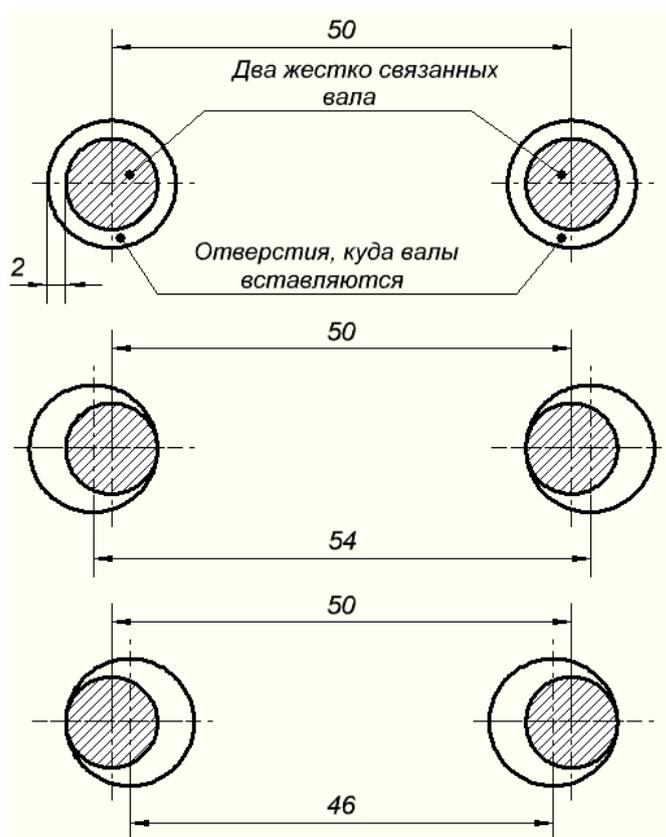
К определению значения допуска для межцентровых размеров
